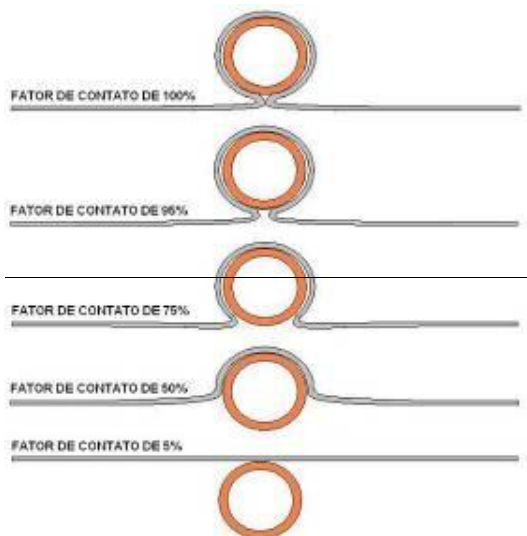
Exemplos de fator de contato entre Placa Absorvedora e Serpentina
